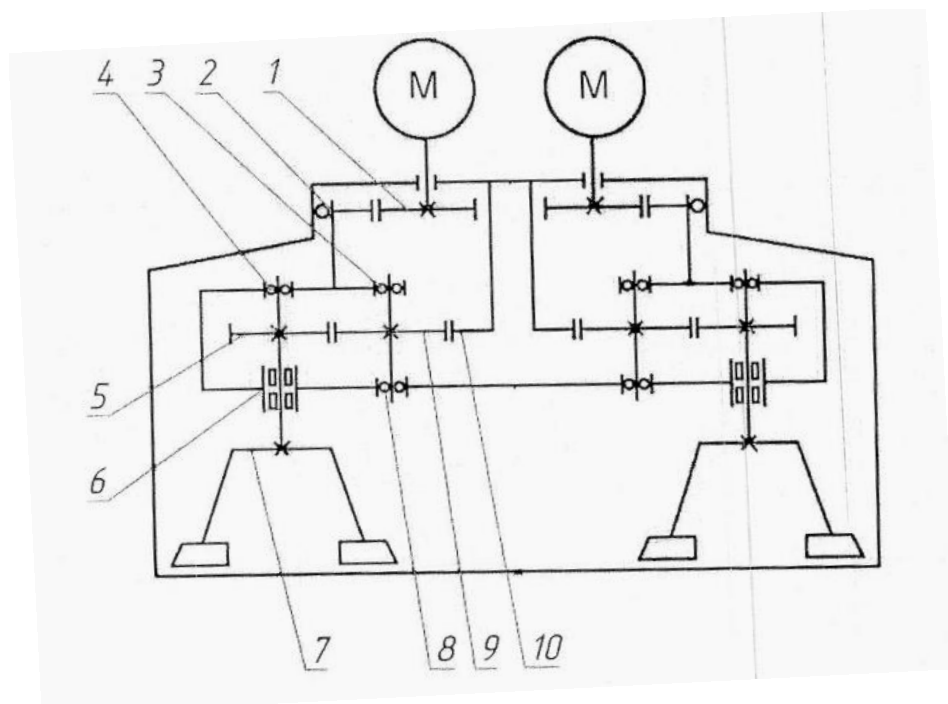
Кинематическая схема смесителя СБ – 242 – 8М: 1, 5, 9, 10 – зубчатые колеса; 2, 3, 4, 6, 8 – подшипники, 7 – смесительные лопатки.
